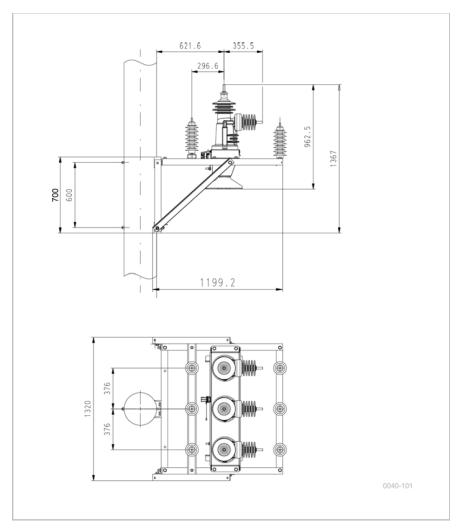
Подстанционная рама тип Е - габаритные размеры
